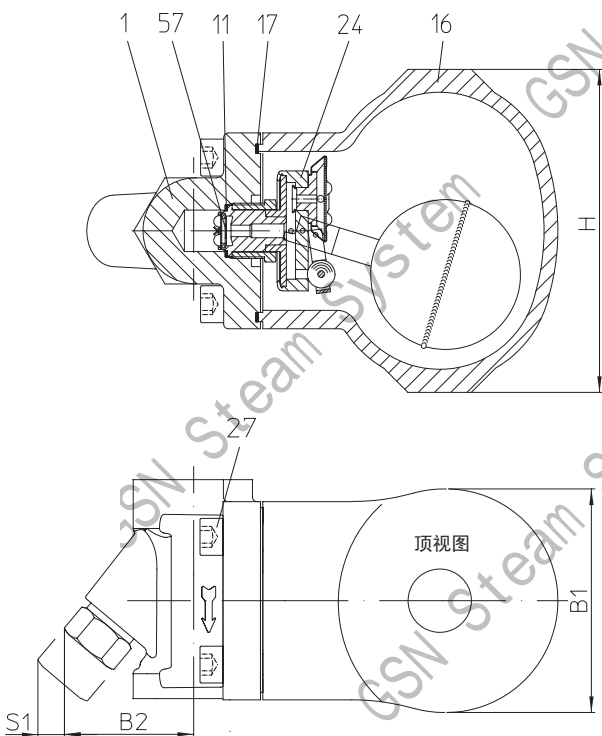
2 (PN 40) 螺纹连接 水平安装
